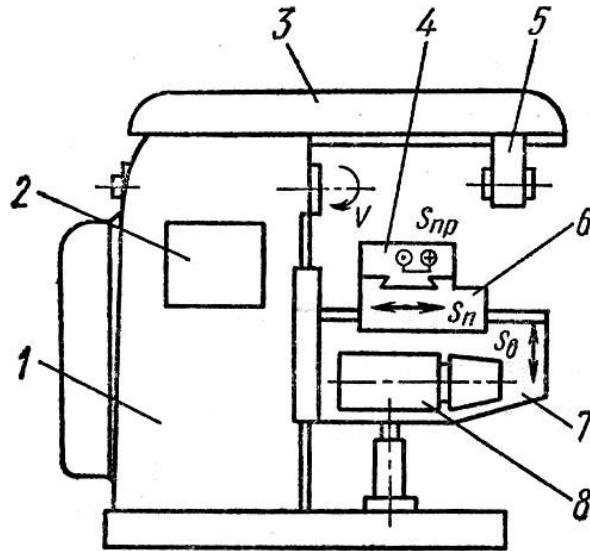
Загальний вигляд горизонтально-фрезерного верстату
